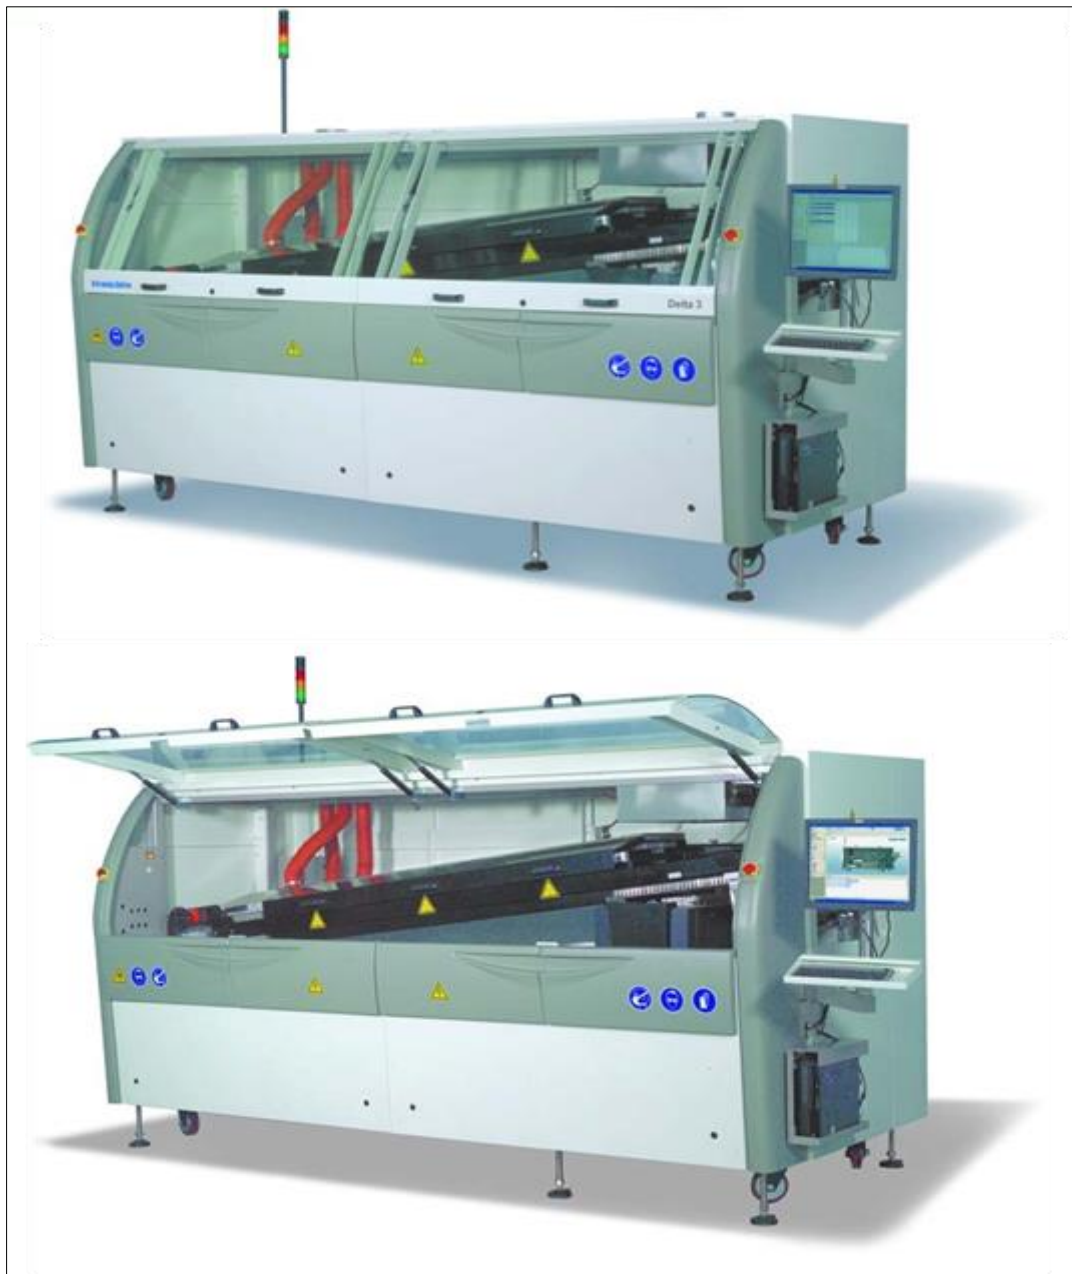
Soldadora por ola con la puerta cerrada y abierta
